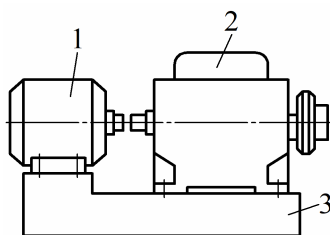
Схема размещения электродвигателя и редуктора на раме
